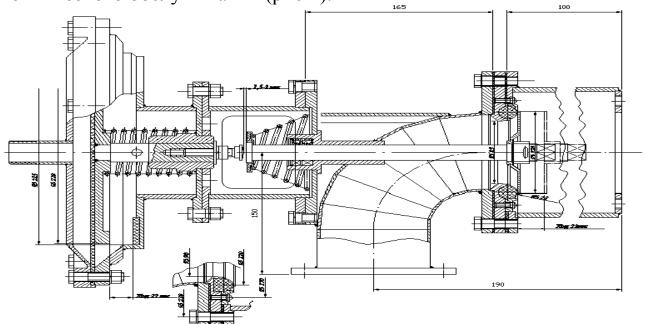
Модернизированный диафрагменный дифференциальный пневмопривод подачи сжатого воздуха к узлам камерного питателя
